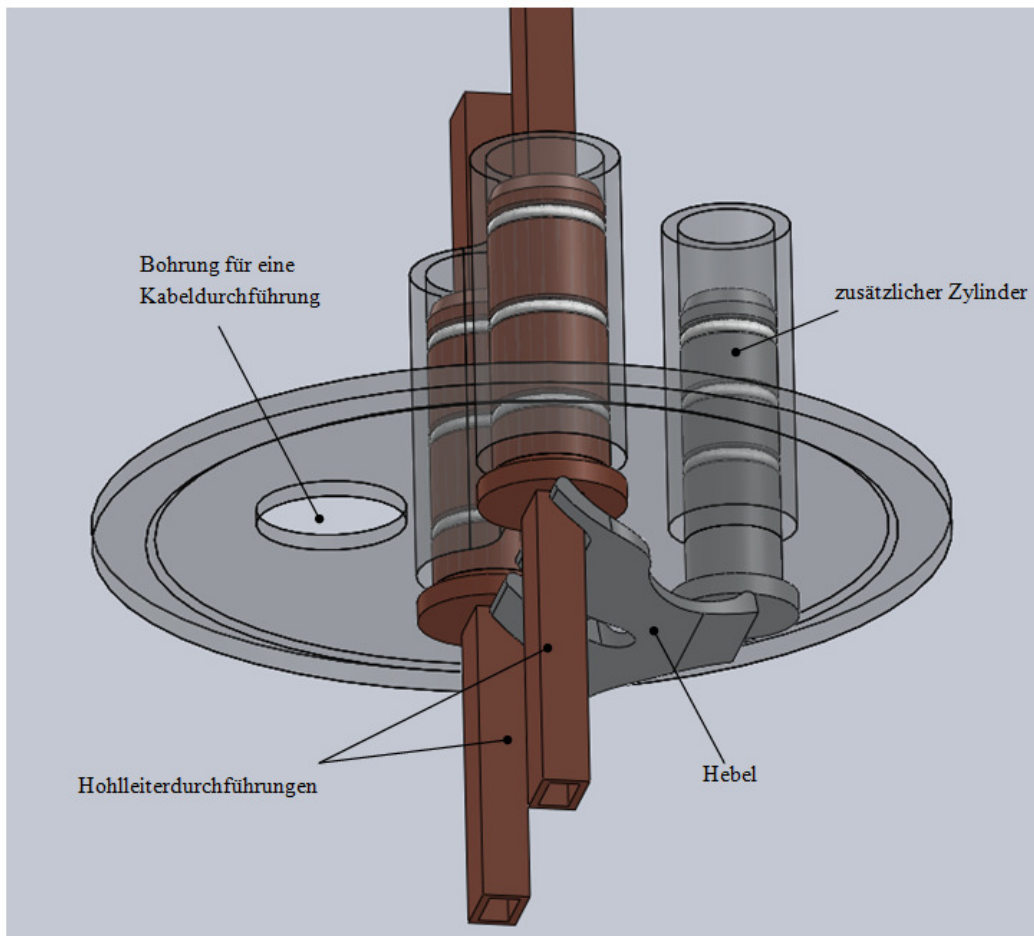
Montagedeckel mit Längenausgleich und einer Bohrung für die Kabeldurchführung
